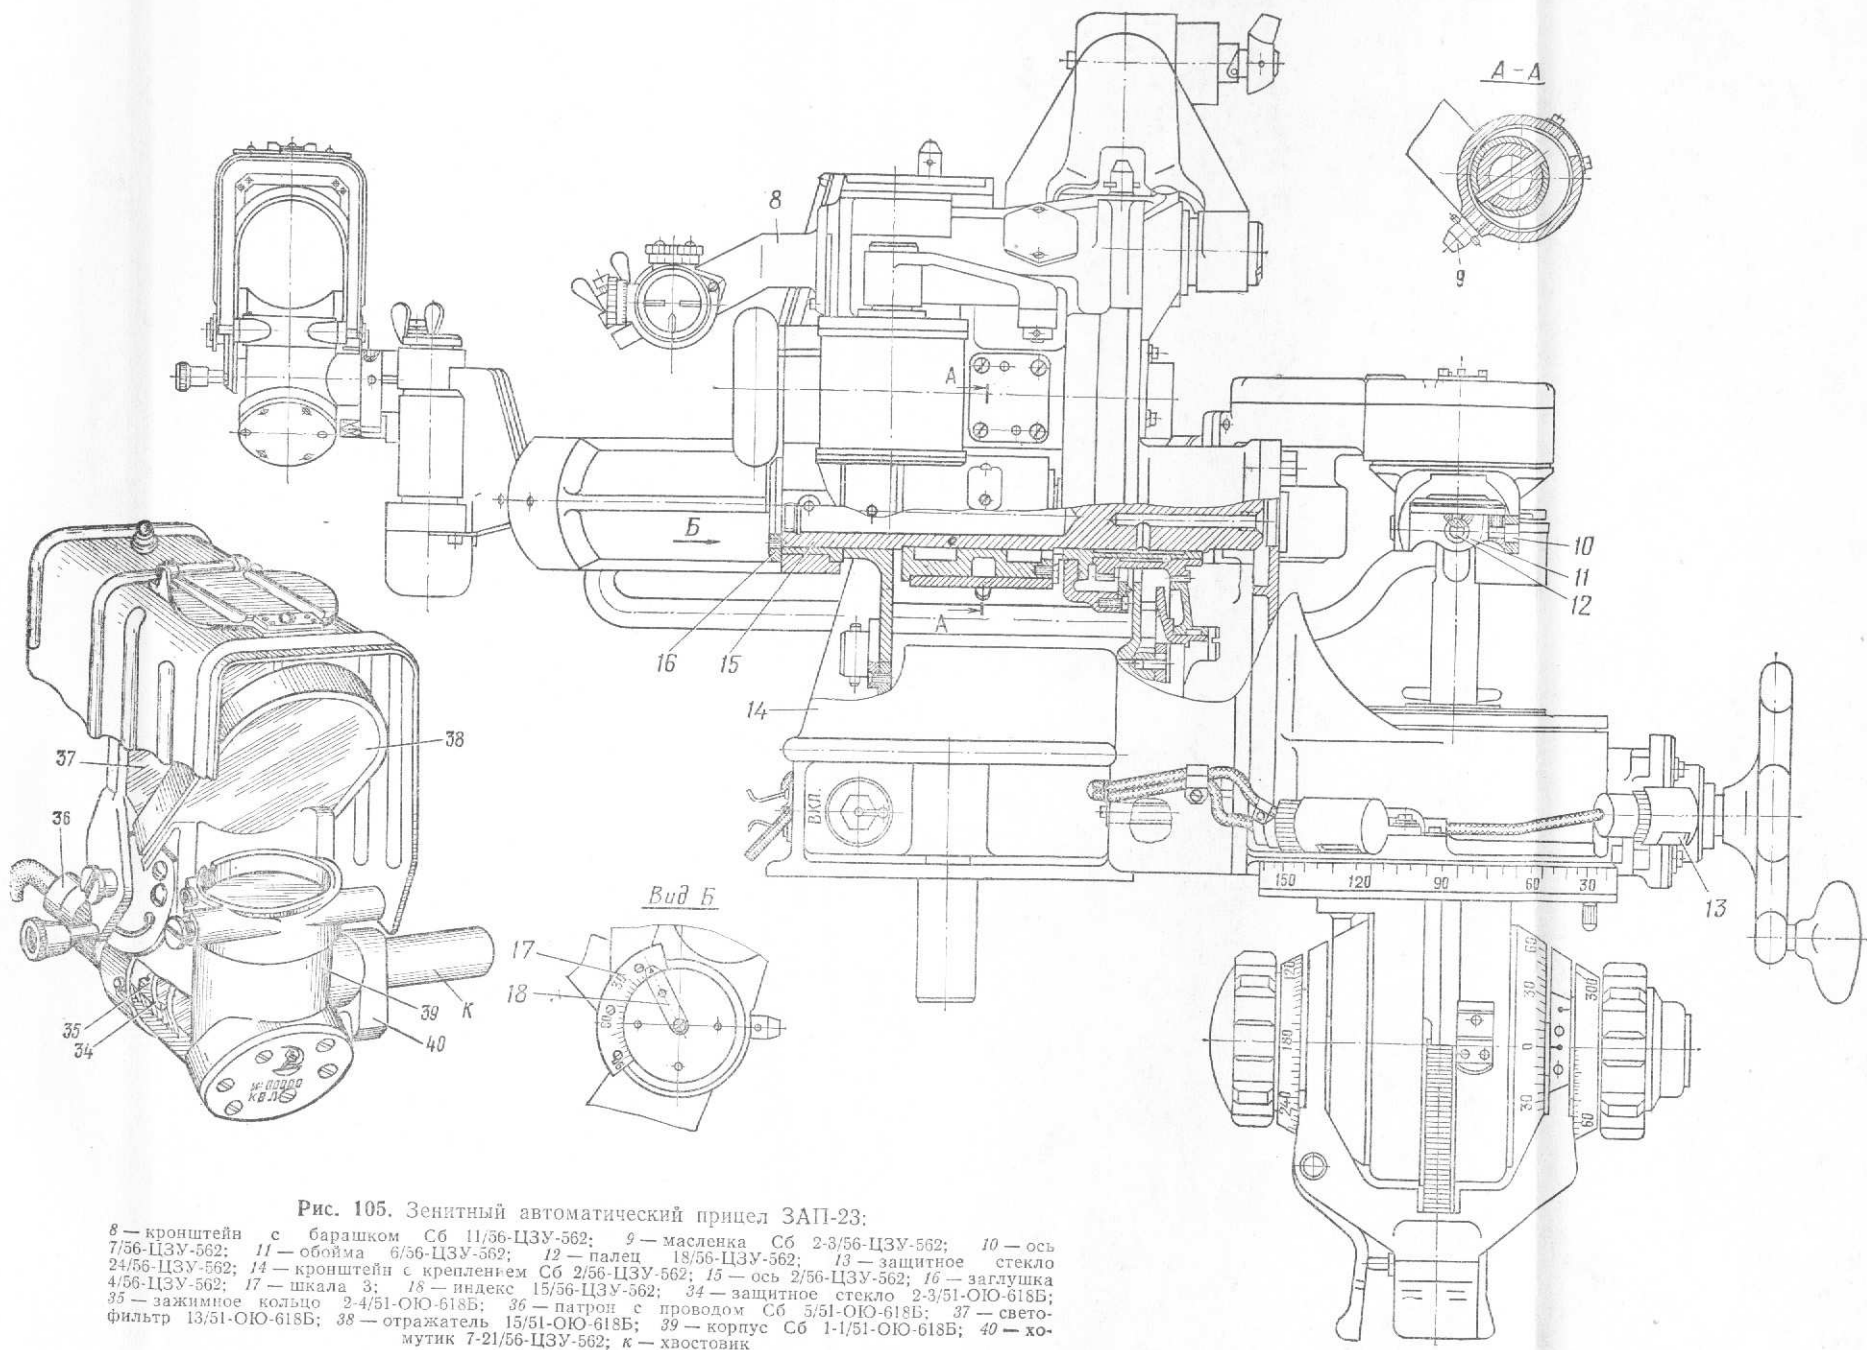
Зенитный автоматический прицел ЗАП-23;
